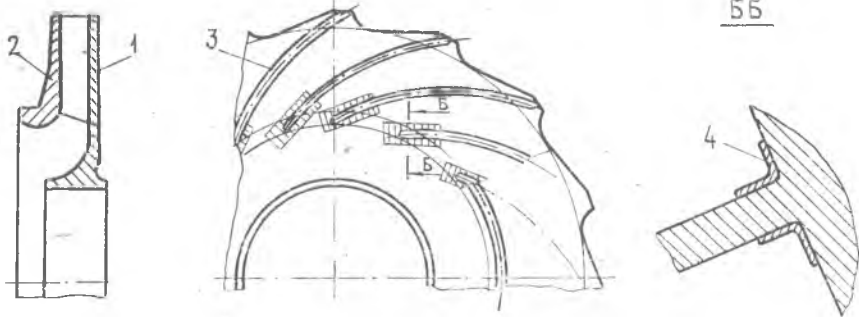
Рабочее колесо: 1 — диск основной; 2 — диск покрывной; 3 — лопатка; 4 — шликер ВКМ-65
